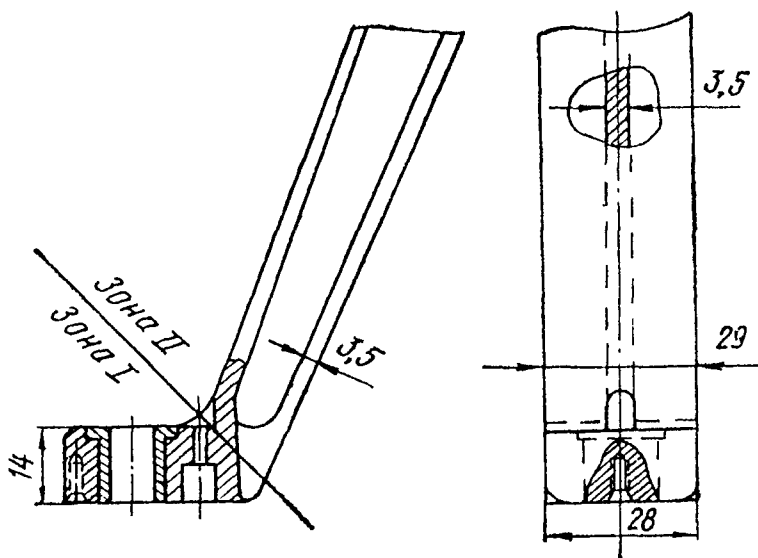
Минимальные размеры ножки пассажирского кресла при зачистке коррозии
